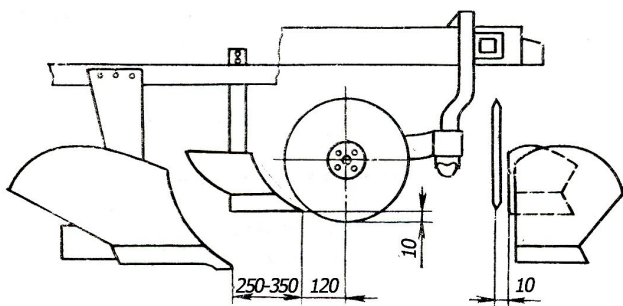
Схема встановлення передплужника і дискового ножа на плугі
